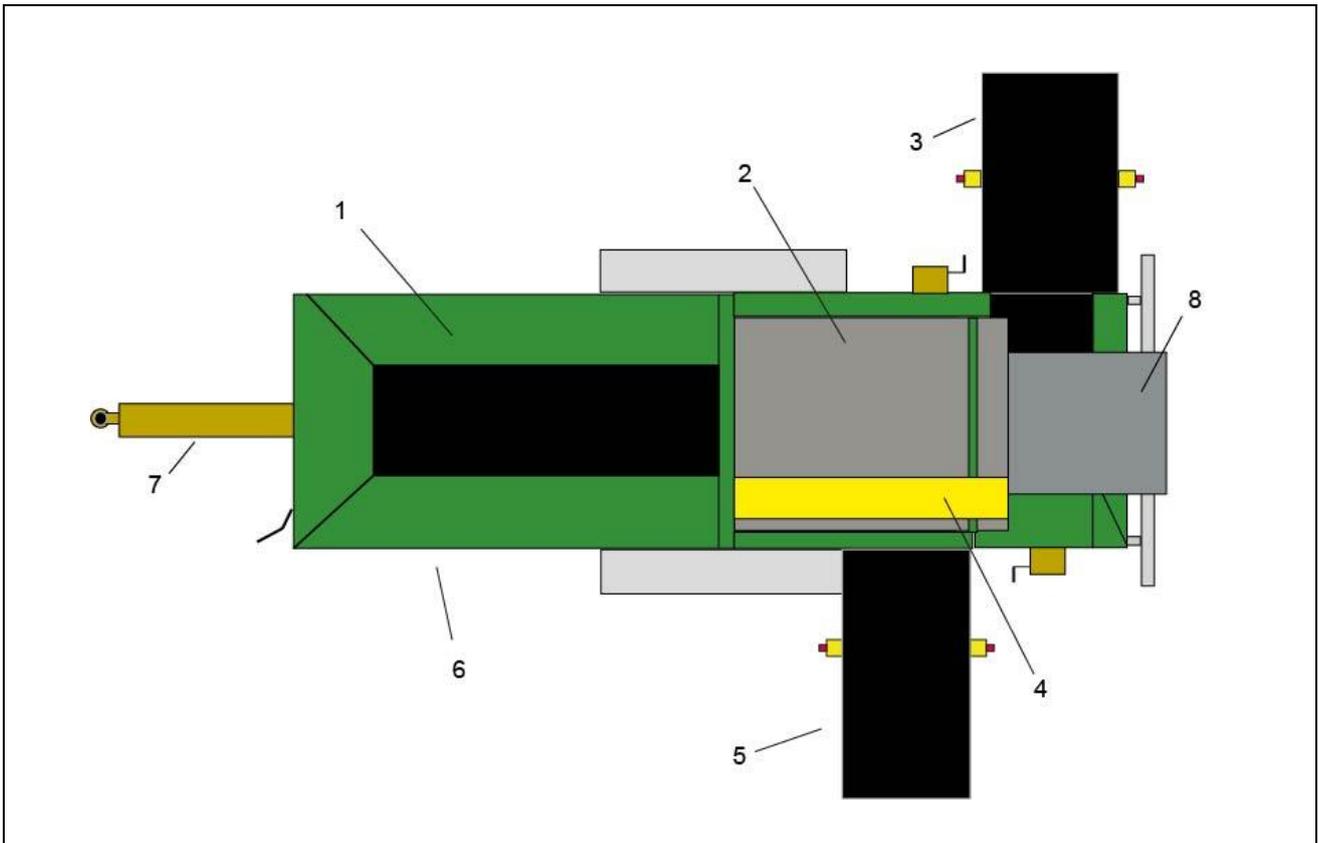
Vue d'ensemble des modules (vue de dessus)
